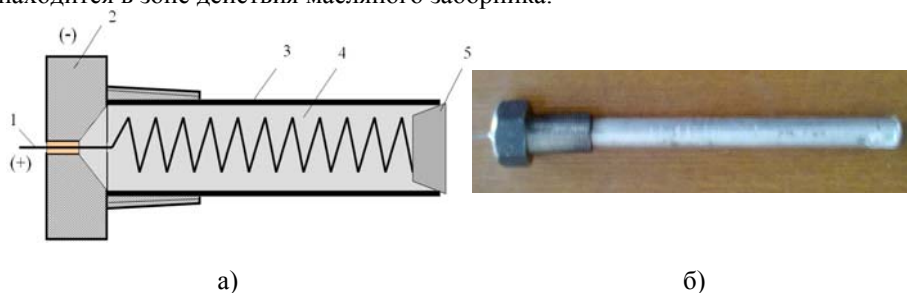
Устройство для разогрева моторного масла: а – схема устройства; б – внешний вид устройства; 1 – спираль; 2 – штуцер; 3 – корпус; 4 – кварцевый песок; 5 - пробка
